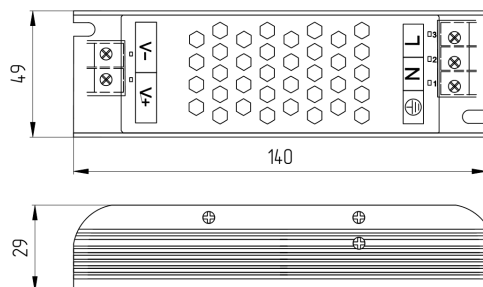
Габаритные размеры блока питания Geniled GL-12V100WM20 Slim.
